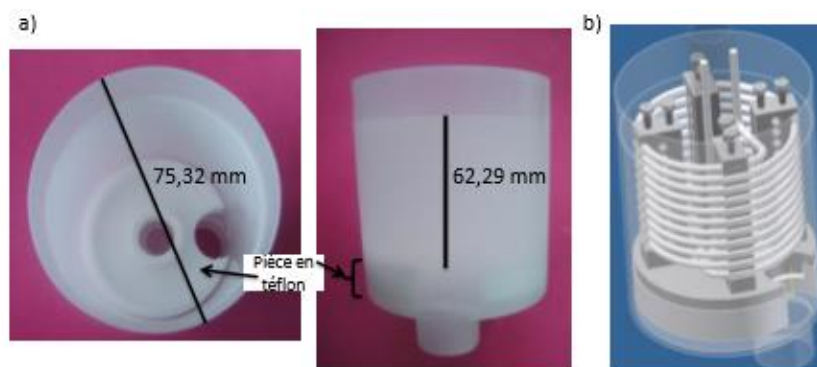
a) Dimensions de la pièce support cylindrique en téflon, b) dispositif de millifluidique avec la tubulure en téflon.
